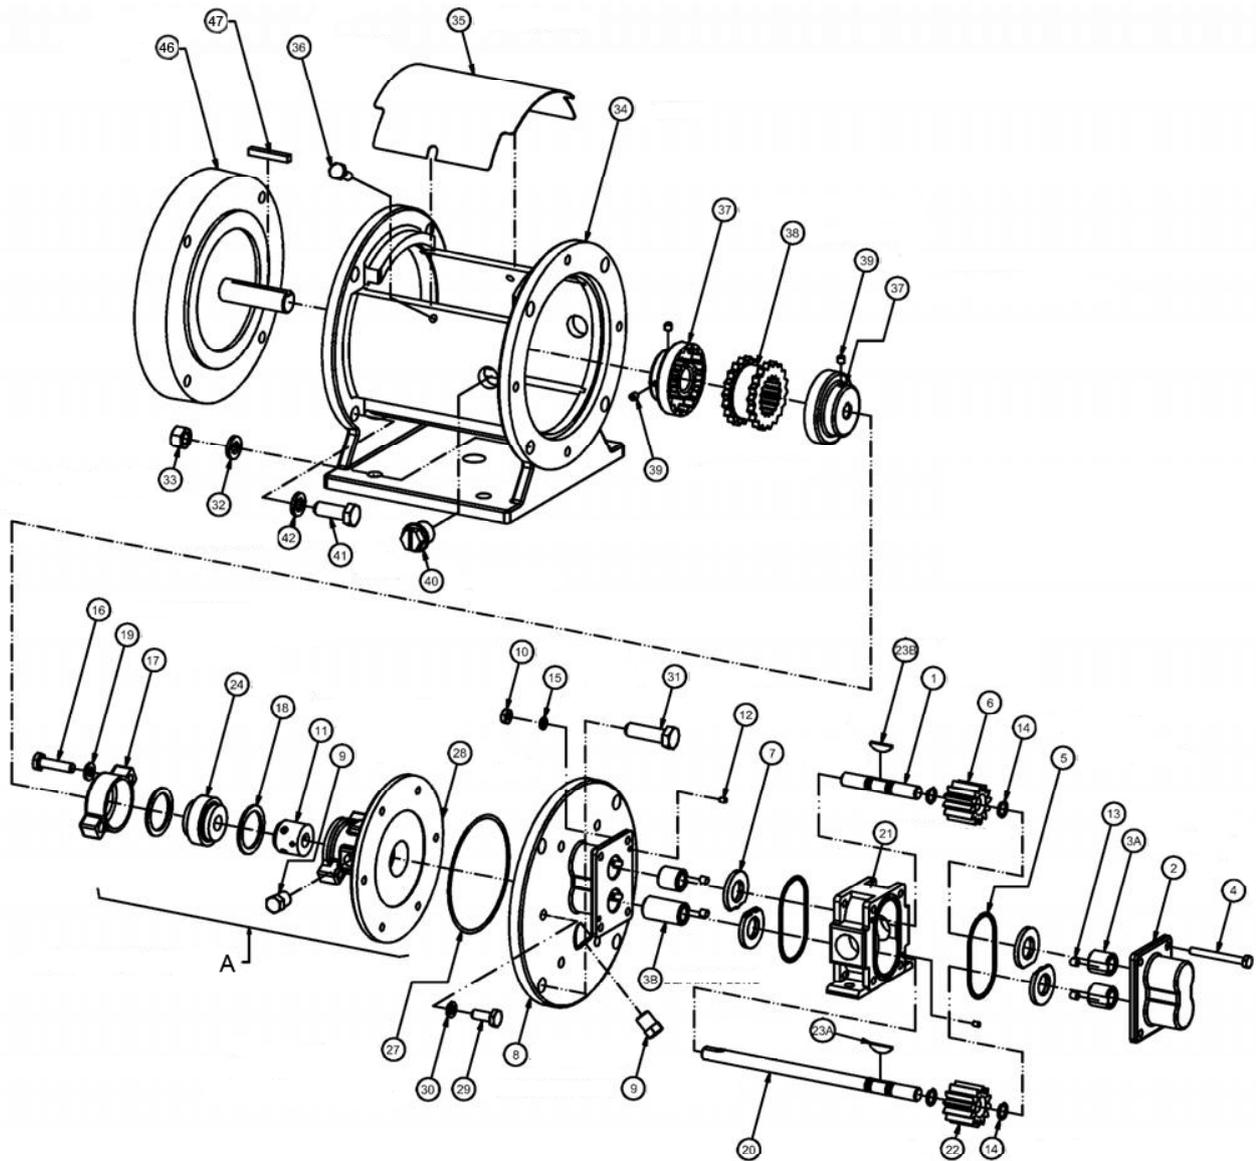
Schnittbild Ausführung mit Gleitringdichtung (Baureihe VGP)
